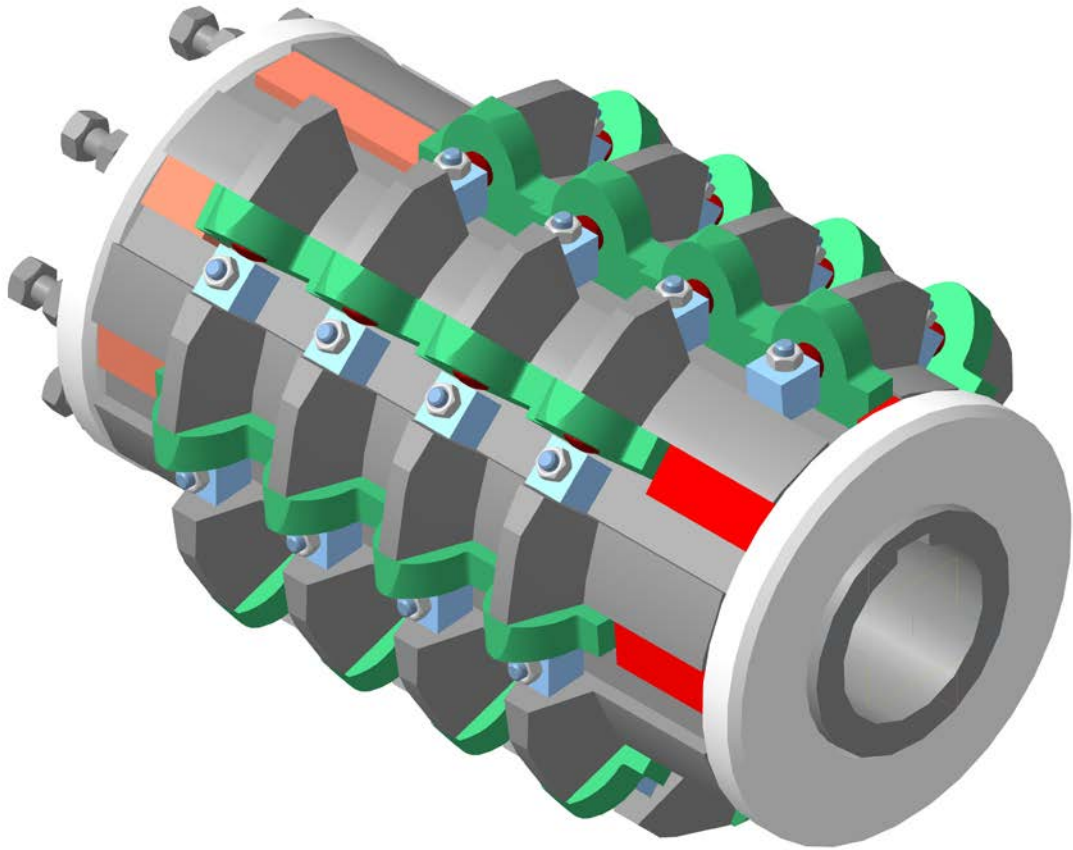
3-Д модель черв'ячної фрези з профілем Новікова.
